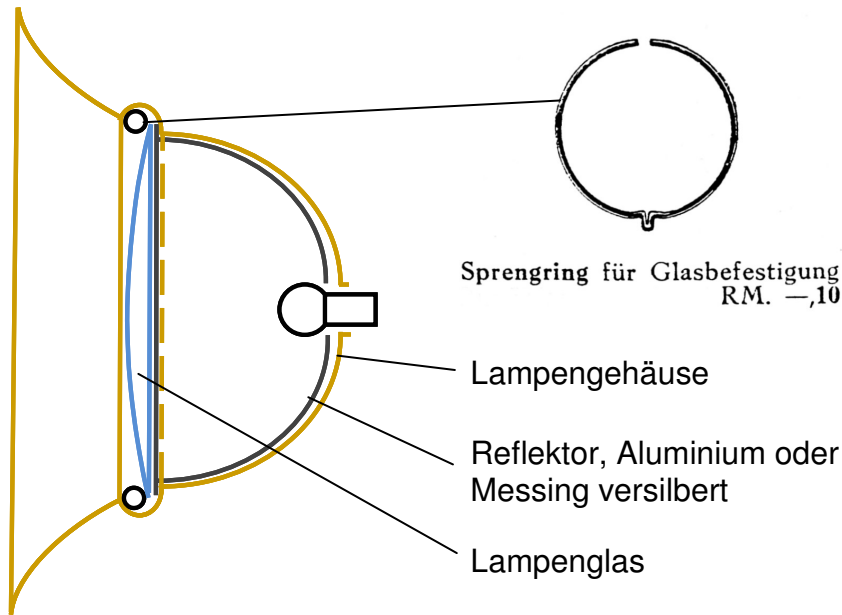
Prinzipieller Querschnitt des Scheinwerfers
